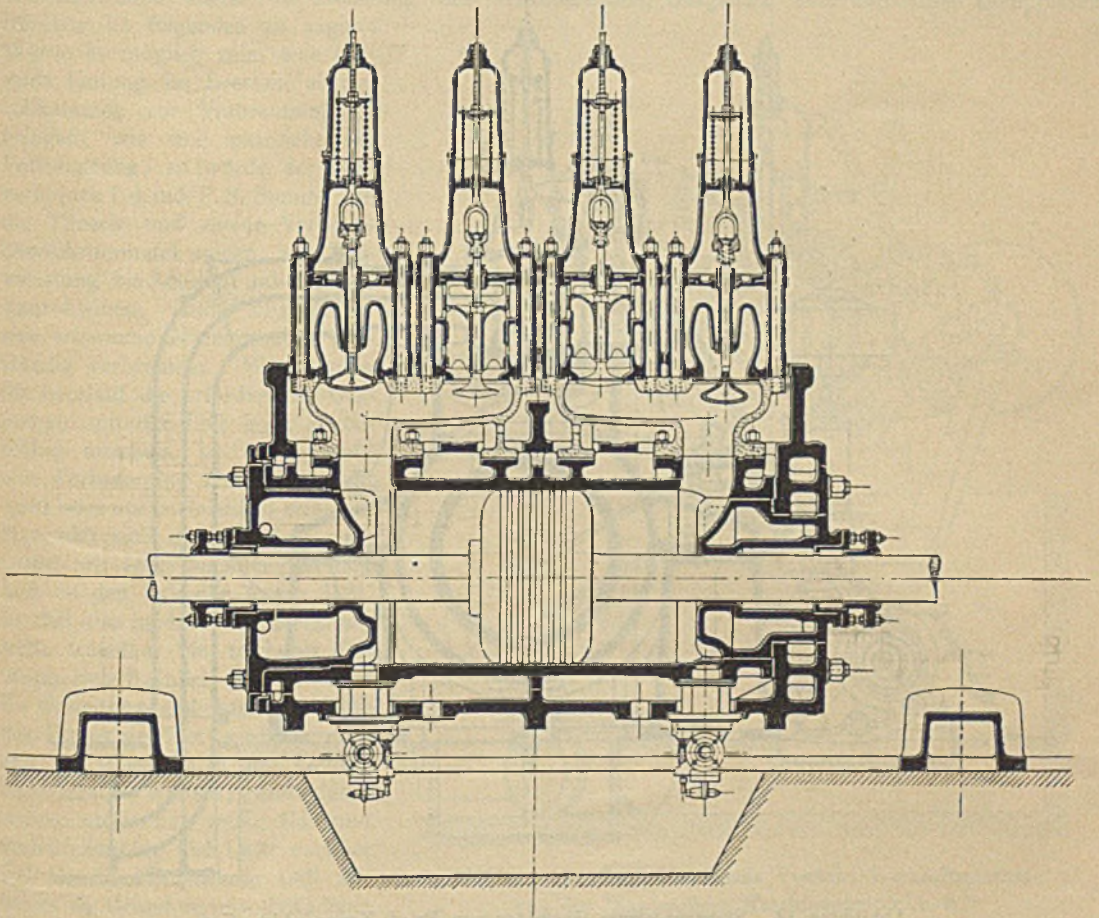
Zylinder zum Gasmotor von Fried. Krupp, Akt.-Ges.
